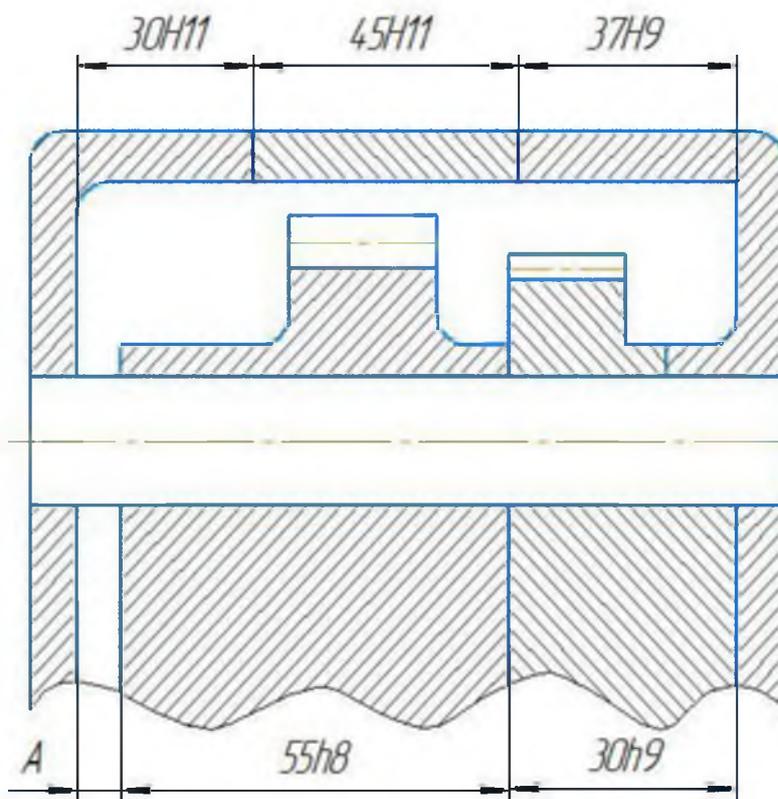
Конструктивная схема узла редуктора с указанием размерной плоской цепи
